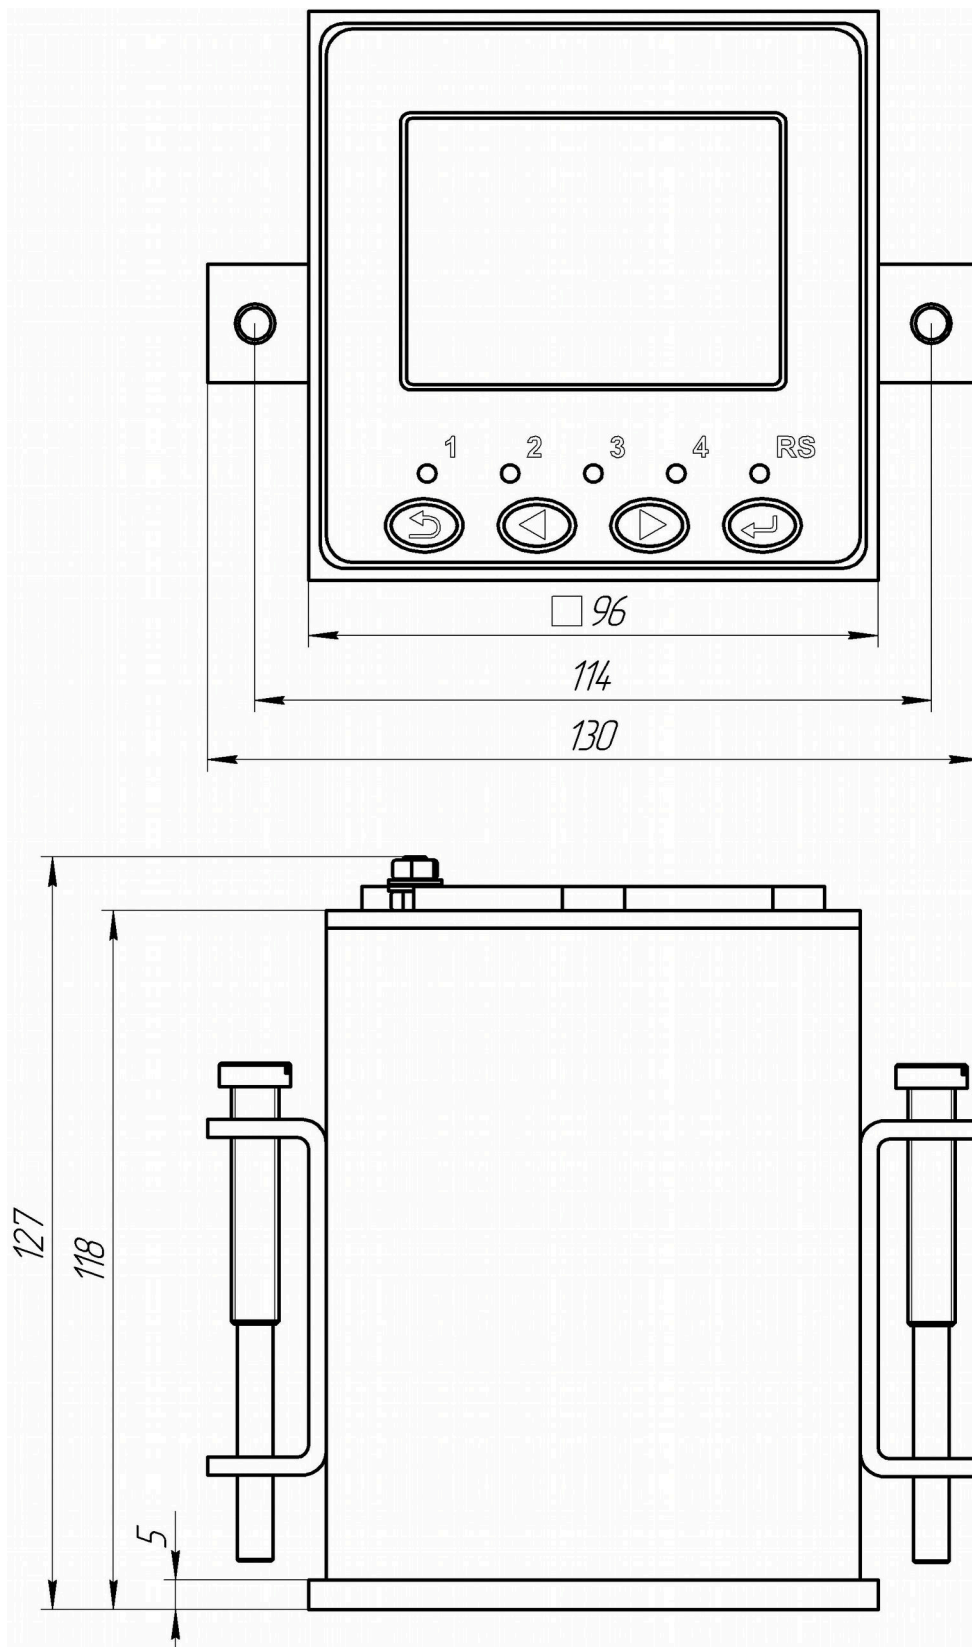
Габаритные размеры корпуса анализатора щитового исполнения
